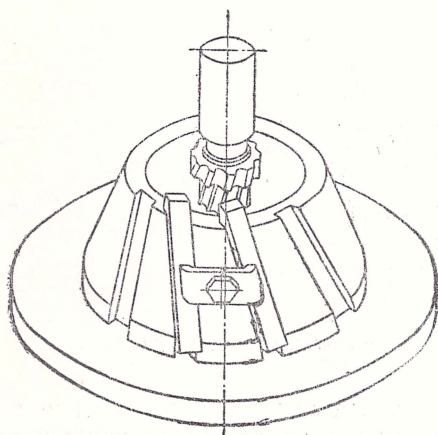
Схема приспособления ротационного типа для фрезерования резцов
